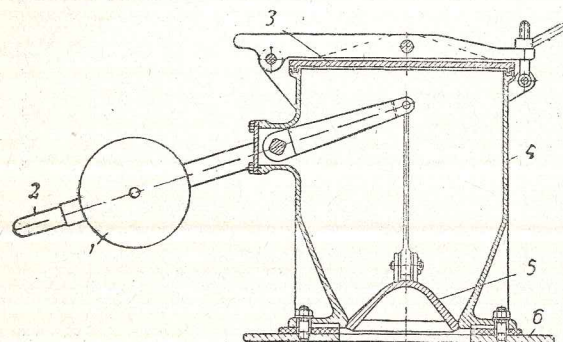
Загрузочная коробка с двумя язычковыми затворными клапанами:
